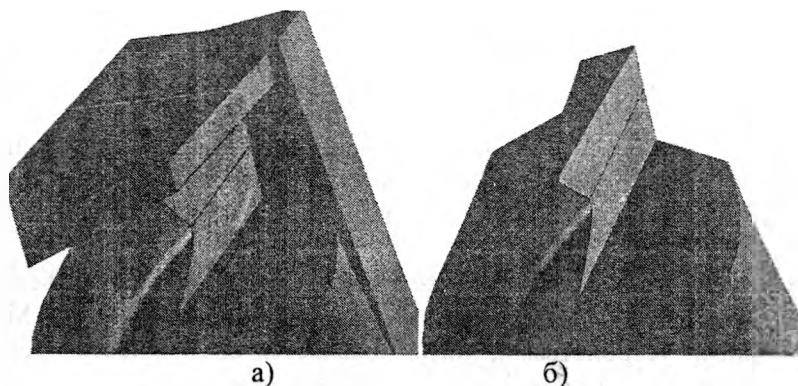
Режущая часть готового сверла. а) тела-инструменты для формирования задней поверхности, б) режущая часть сверла
